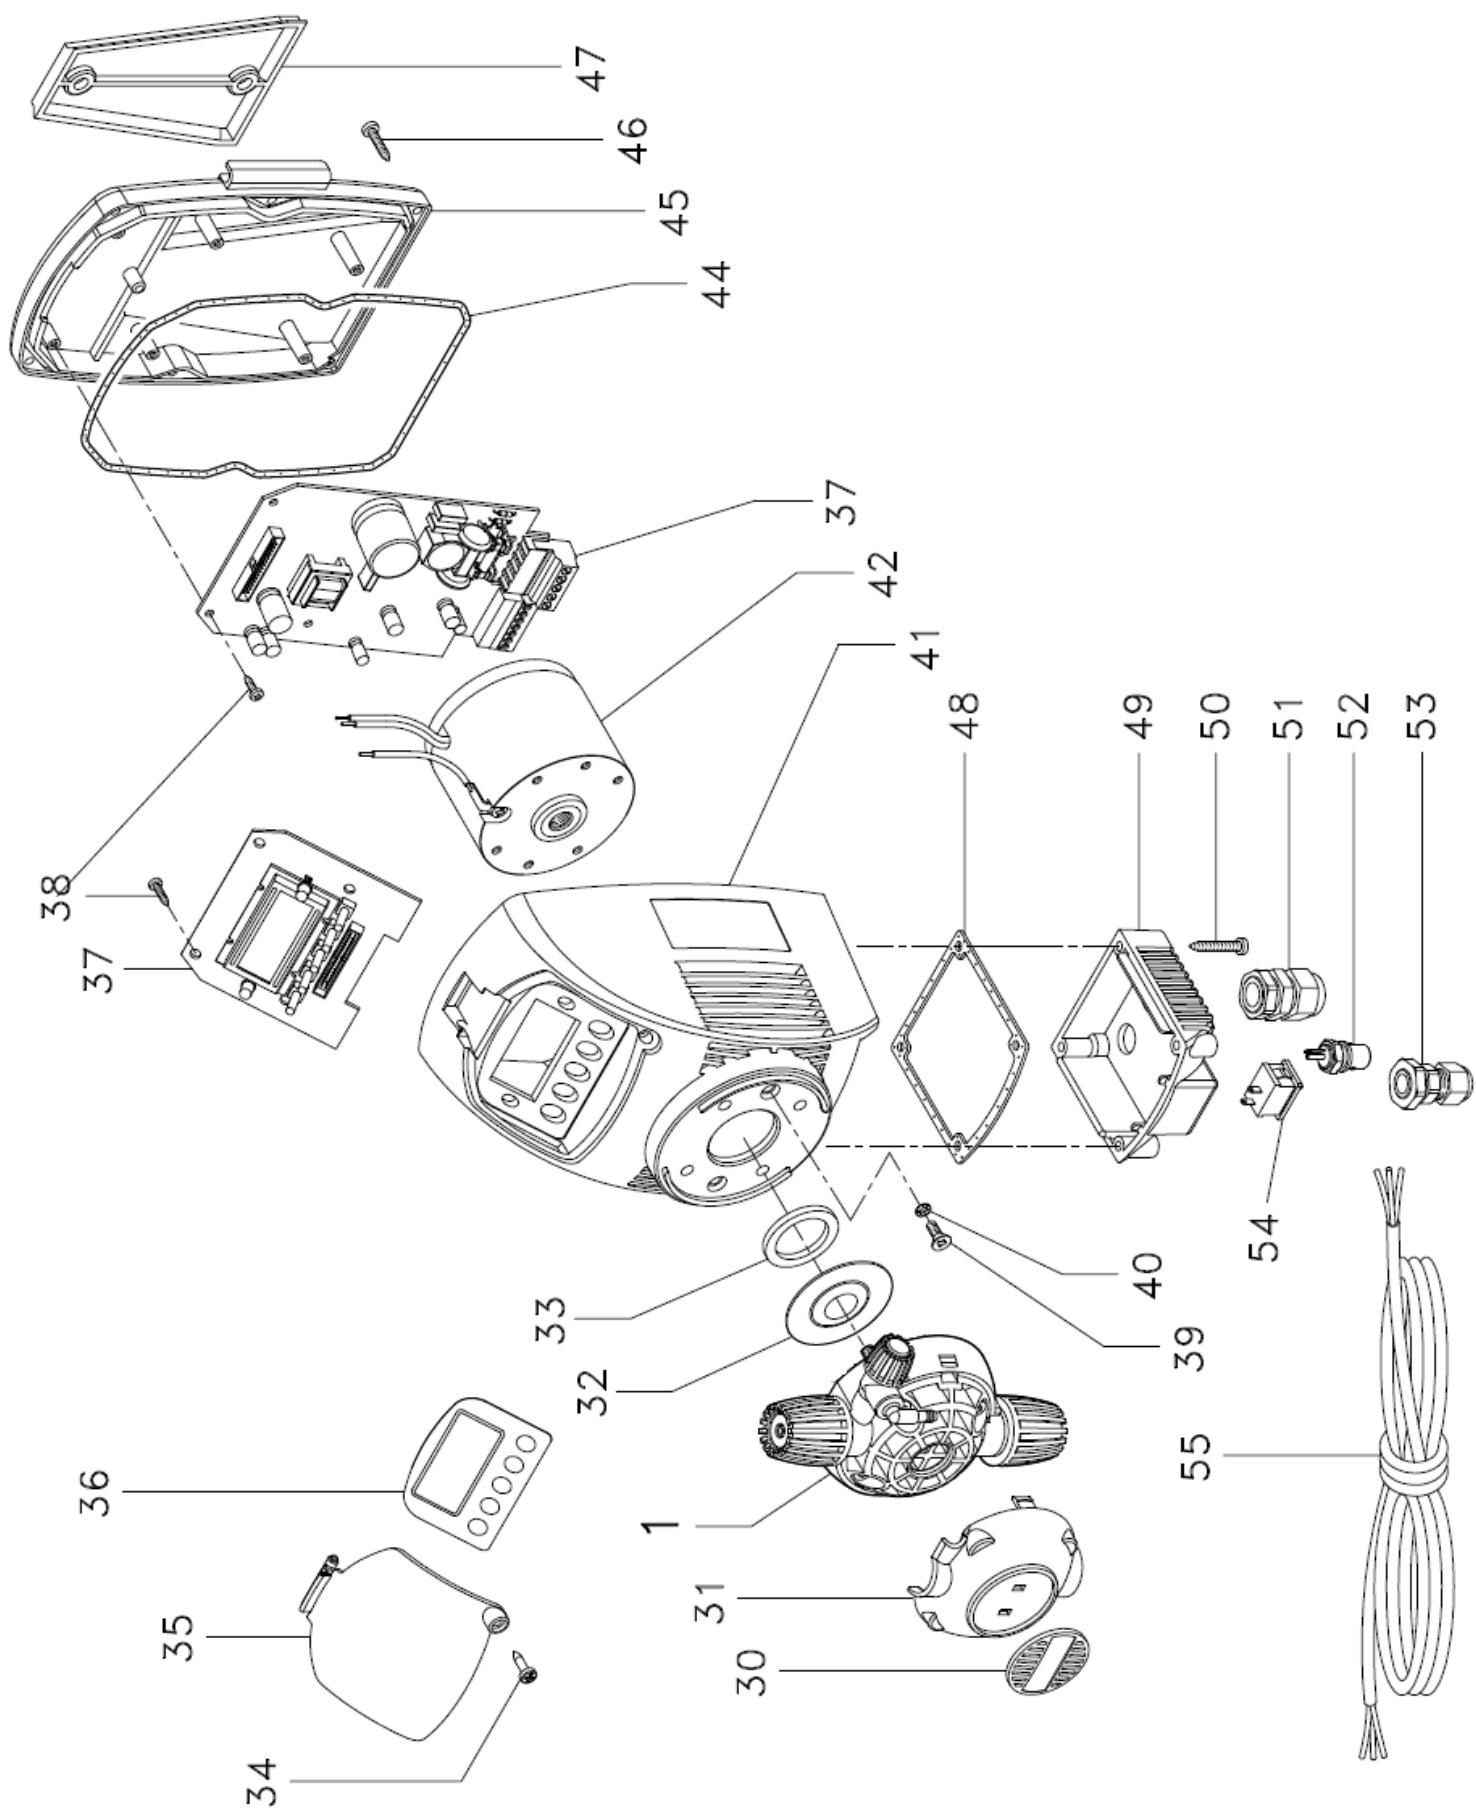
SERIE HC 897 - Espreso / Opis / Explode / Dibujo / Explosionszeichnung / Чертеж
